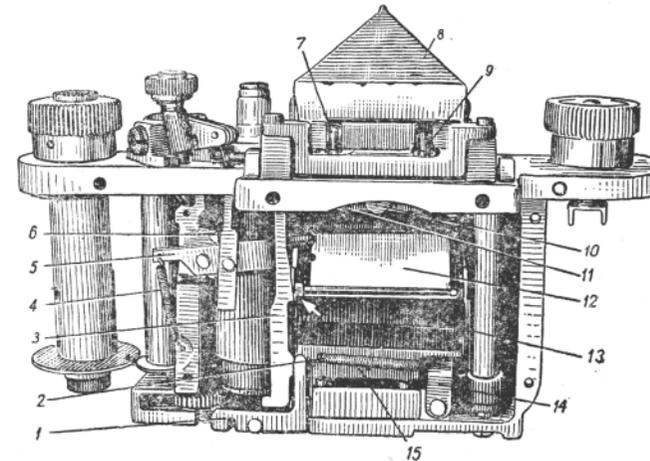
Зеркальный видоискатель и детали механизма привода зеркала.
